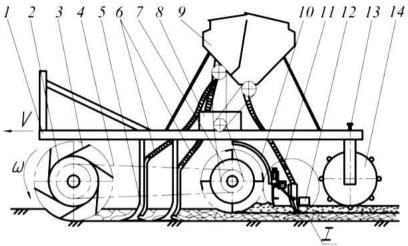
Агрегат для предпосевной уборки почвы и посева (вид сбоку)
